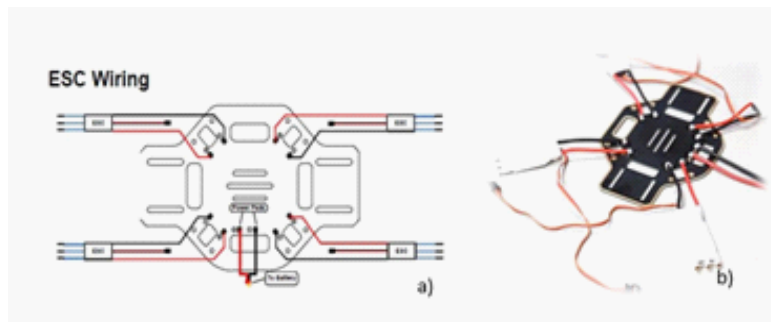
ESC: a) Puntos de soldadura y b) ESC's soldado. (Fuente: <https://sites.google.com/site/makingdrones/home/build>)
